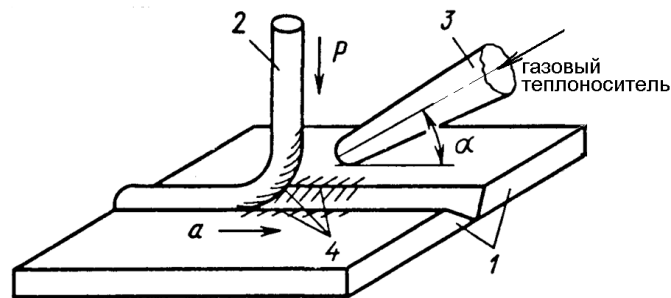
Схема сварки газовым теплоносителем с присадкой:
